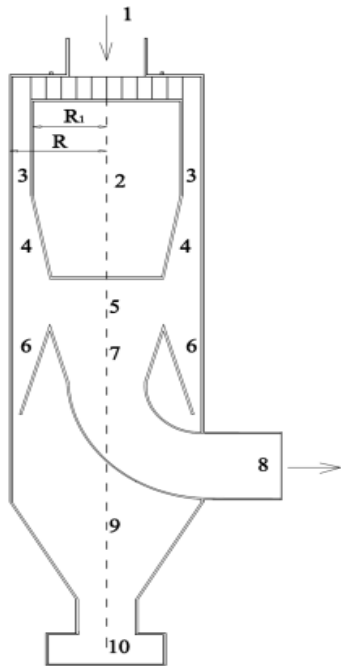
Вид осевого разреза новой конструкции сепаратора
